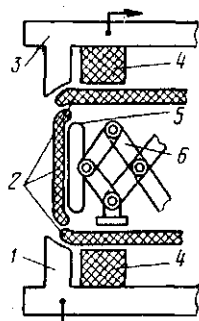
Сваривание изделия пространственной формы (объемная сварка):
